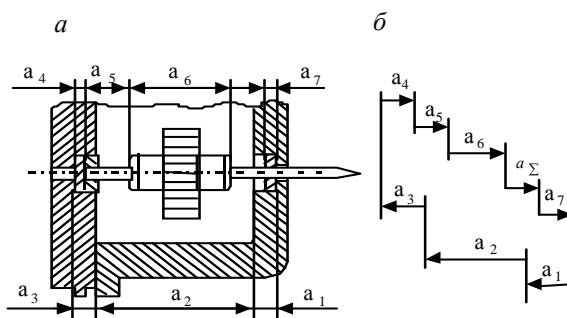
Чертеж сборочной единицы (а) и размерной цепи (б)
